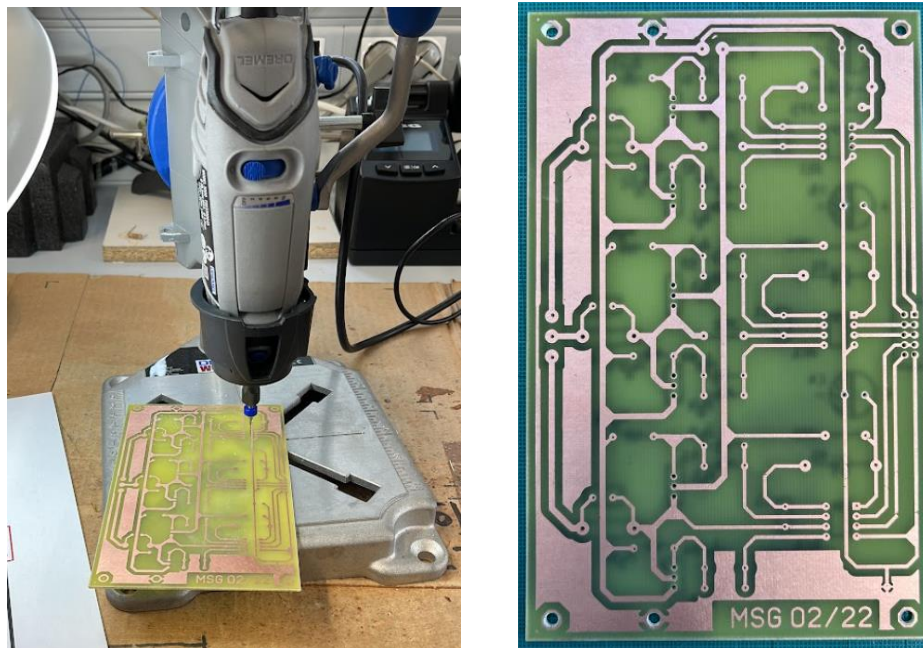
Taladrado de la PCB mediante miniherramienta. Fuente [Propia]
